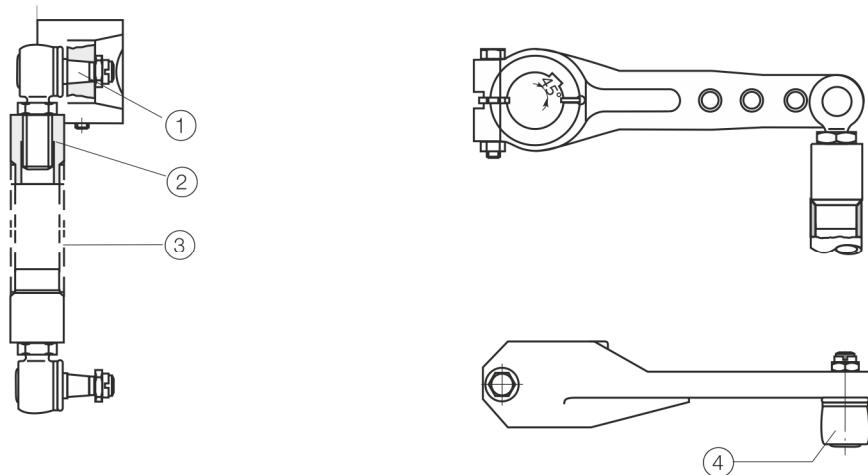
Componentes da haste de acoplamento e dimensões do tubo de ligação
